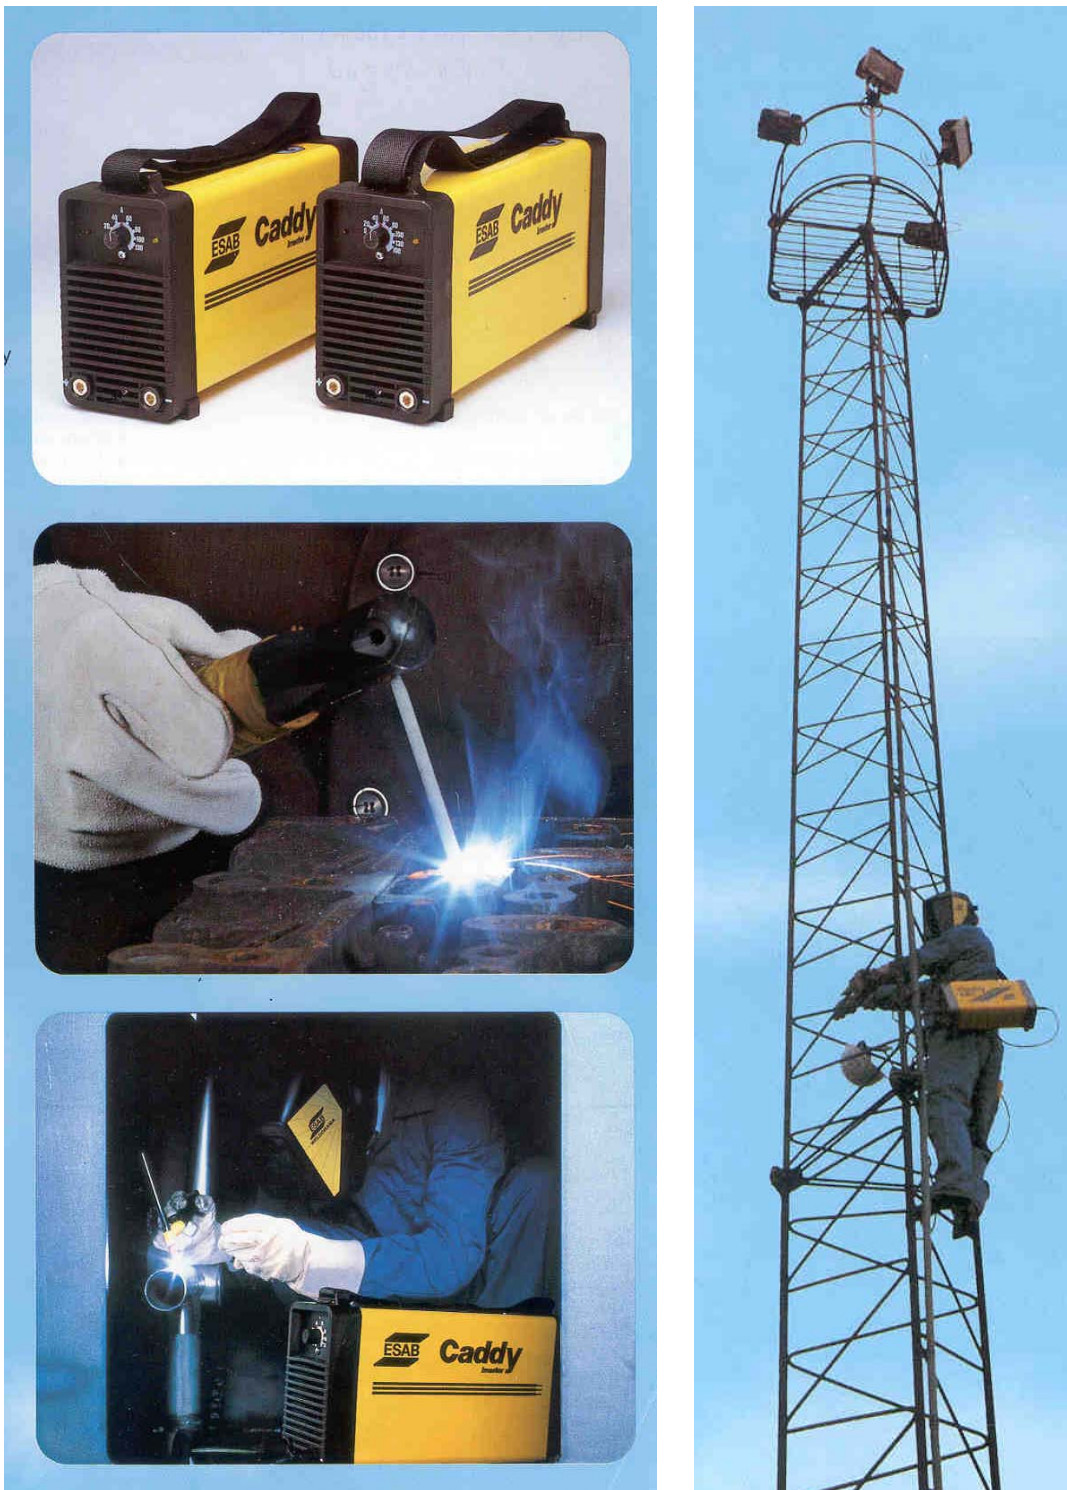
Catálogo de fonte inversora, capaz de soldar por eletrodo revestido e TIG.
